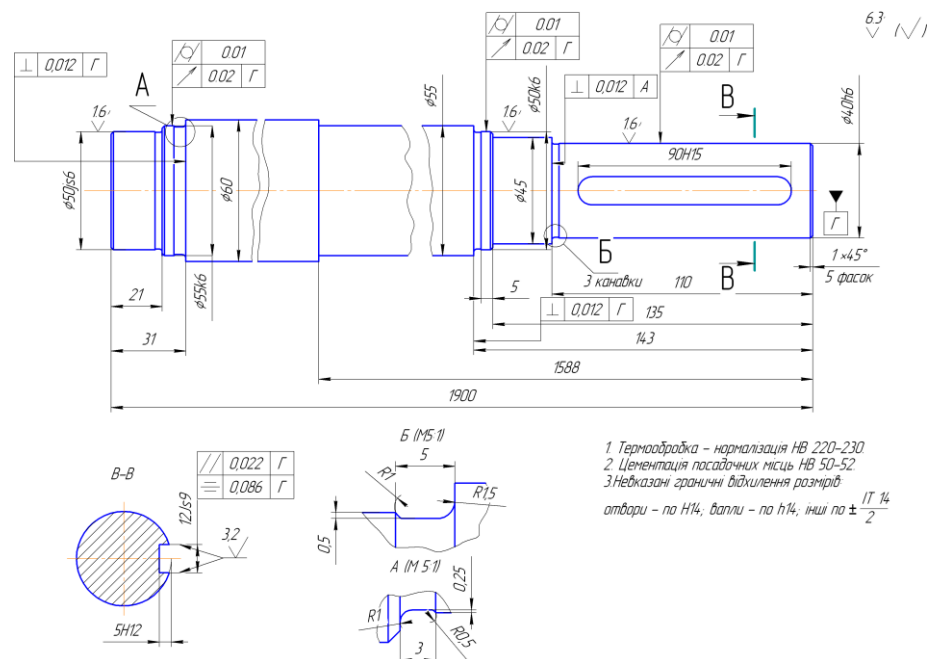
Робоче креслення приводного валу каменевлюювача
